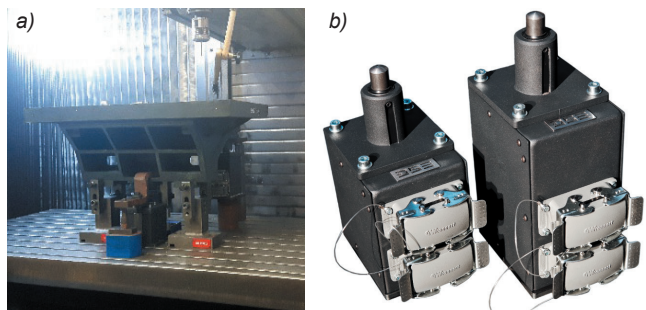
Położenie punktów ustalających odlew stołu frezarskiego
